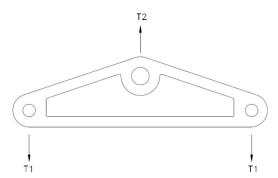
Detalhe para indicação de esforços aplicados para execução dos ensaios
